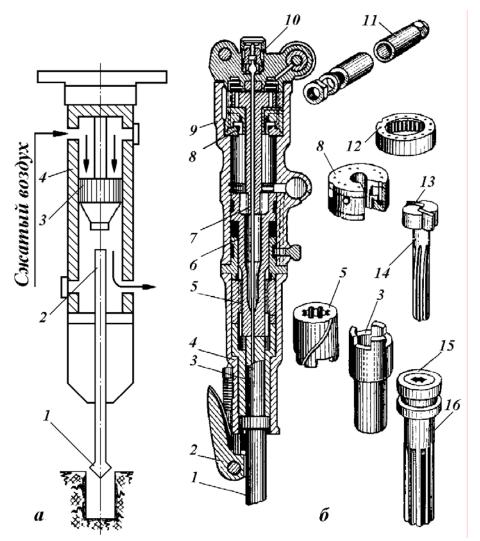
Схема устройства пневматического перфоратора: a – схема; δ – конструкция перфоратора: l – бур; 2 – буродержатель; 3 – поворотная муфта; 4 – корпус поворотного механизма; 5 – ведущая муфта; 6 – направляющая букса; 7 – геликоидальный стержень; 8 – воздухораспределительное устройство; 9 – корпус; 10 – промывочное устройство; 11 – ручки; 12 – храповое кольцо; 13 – собачка; 14 – головка; 15 – геликоидальная гайка; 16 – шток поршня
